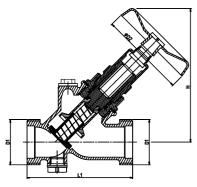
Alwa-KFR mit beidseitigem Außengewinde
